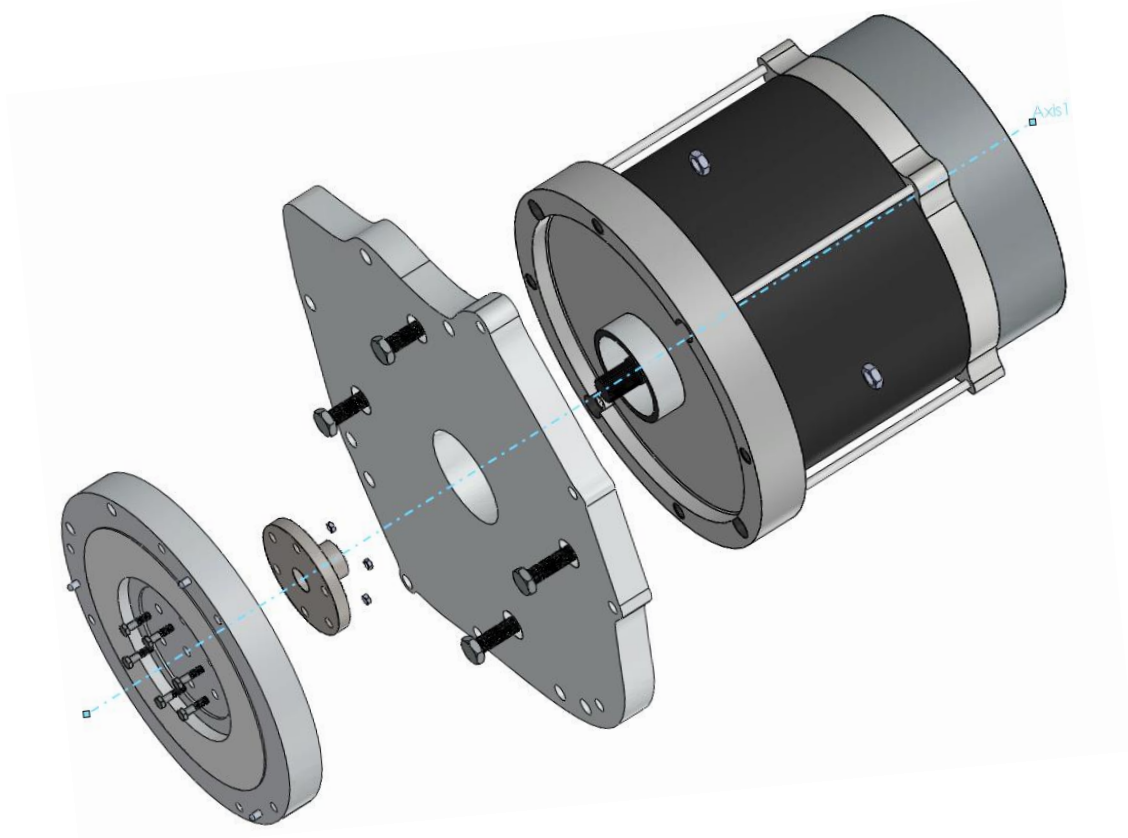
Vista explosionada de la unió de l'útil de fixació, el volant d'inèrcia, la placa adaptadora i el motor.
